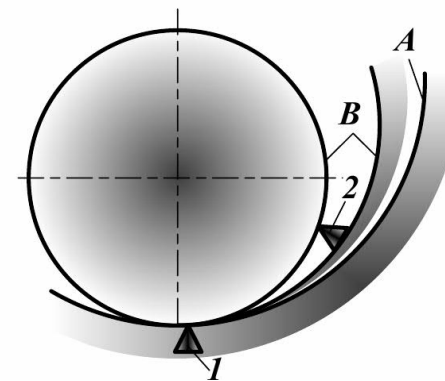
Схема абразивного изнашивания соединения вал-подшипник:
